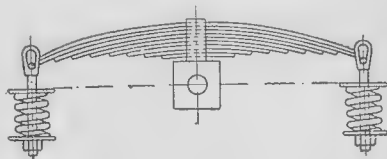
Рессорное подвешивание с вертикальными пружинами.
